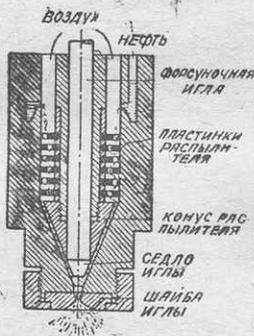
Процесс распыления горючего в форсунке компрессорного двигателя.
